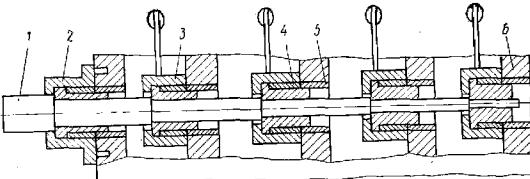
Приспособление для перепрессовки втулок распределительного вала:
